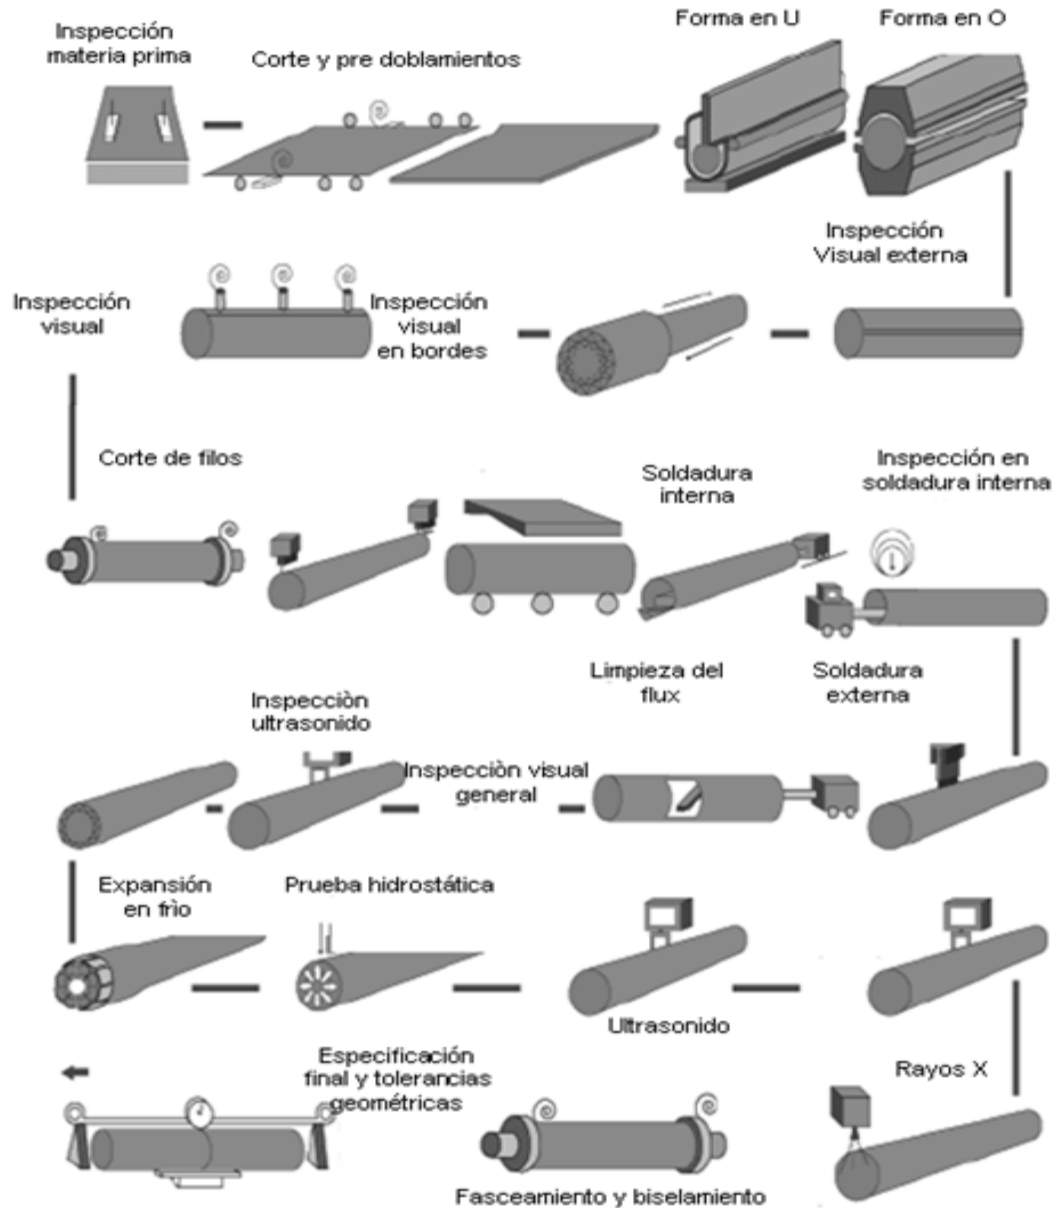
Proceso de fabricación de tubería para la industria petrolera por procesos de soldadura SAW y ERW. [33]
